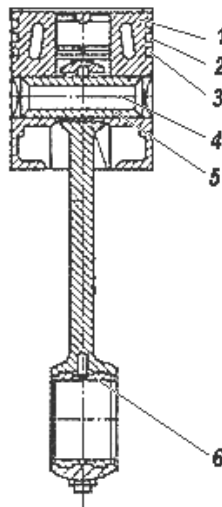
Шатунно-поршнева група не прямоочного компресора: 1 – поршень непрохідний; 2 – компресійне кільце; 3 – масляне кільце; 4 – поршневий палець; 5 – втулка верхньої голівки; 6 – вкладник шатуна
